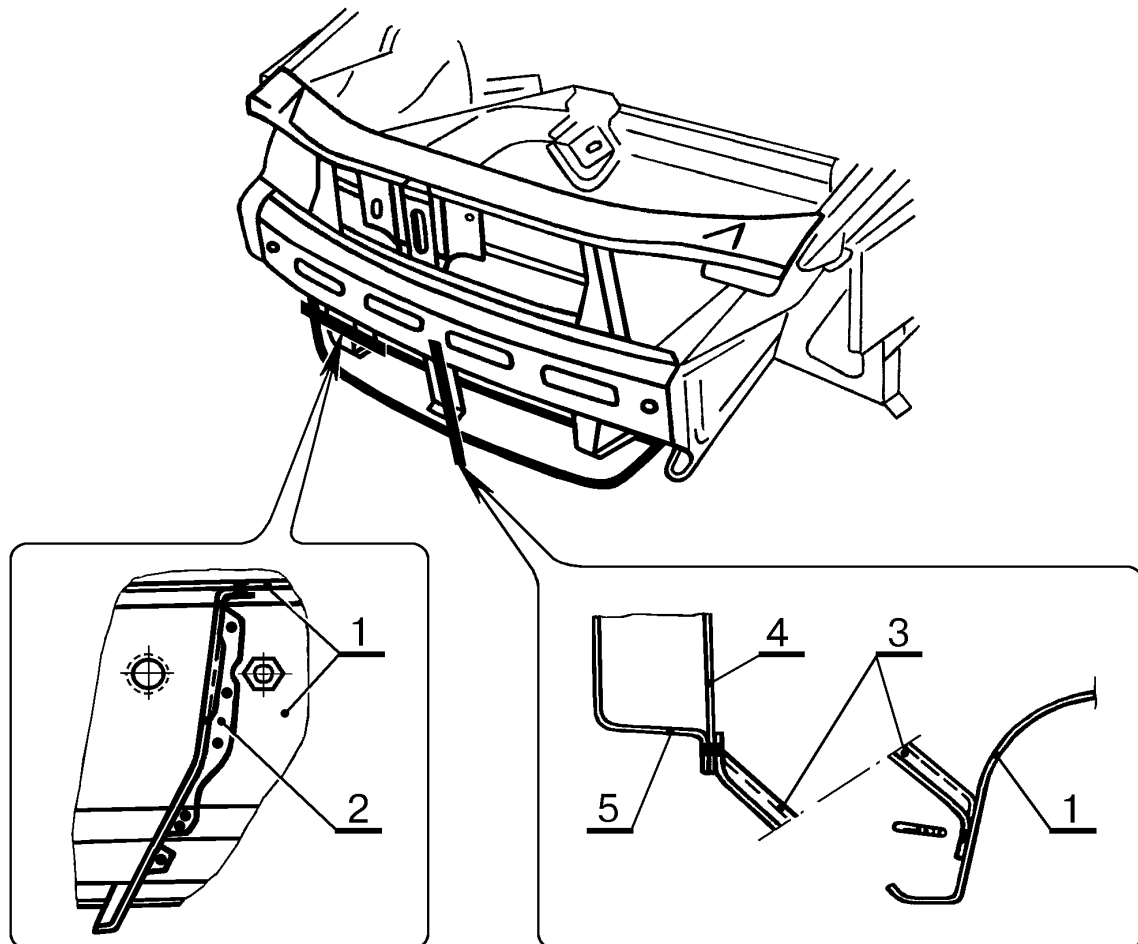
Соединение усилителя рамки радиатора под крепление брызговика двигателя в сборе с сопрягаемыми деталями.
